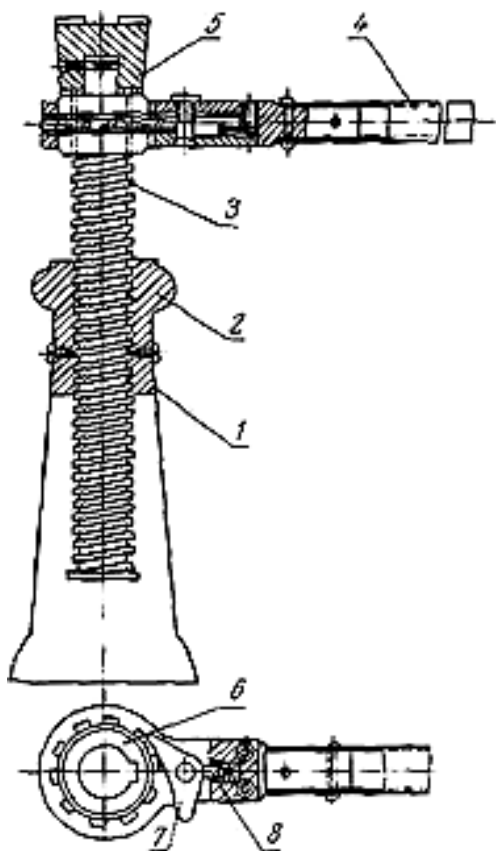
Домкрат винтовой вертикальный с ручным приводом: 1 – корпус; 2 – гайка; 3 – винт; 4 – рукоятка; 5 – опорная пята; 6 – храповое колесо; 7 – собачка; 8 – фиксатор
